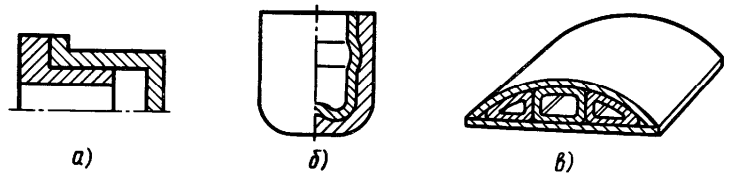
Примеры сварки металлических изделий диффузионной сваркой
